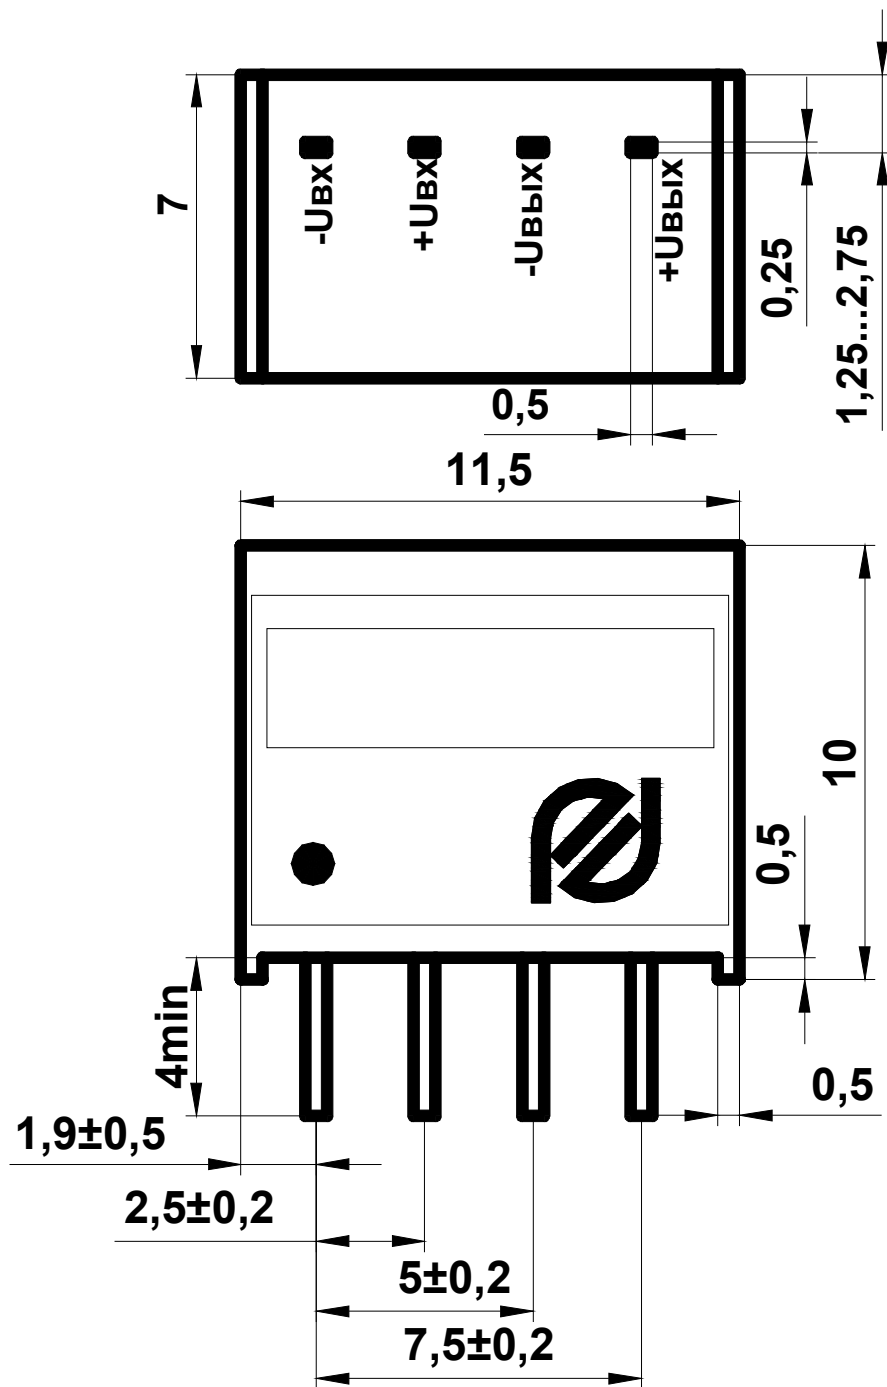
Габаритный чертеж модулей в корпусе «Е»
